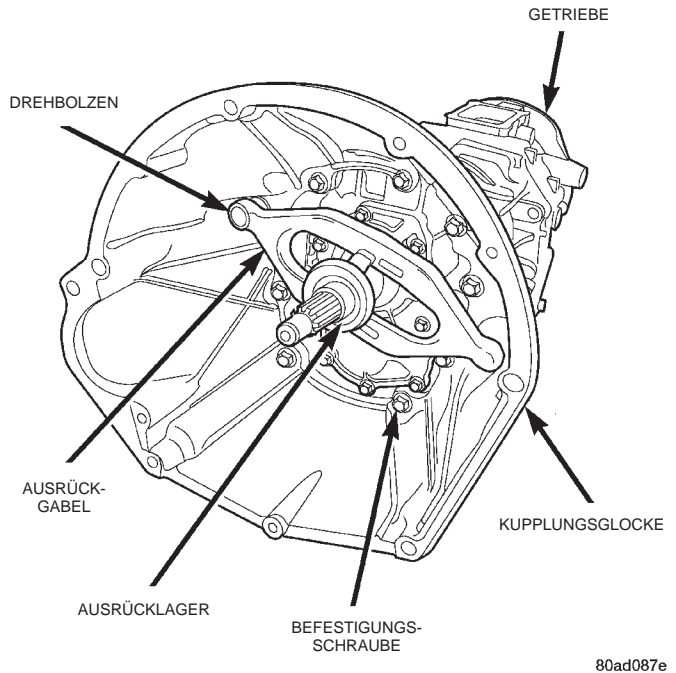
Befestigung der Kupplungsglocke am Getriebe
